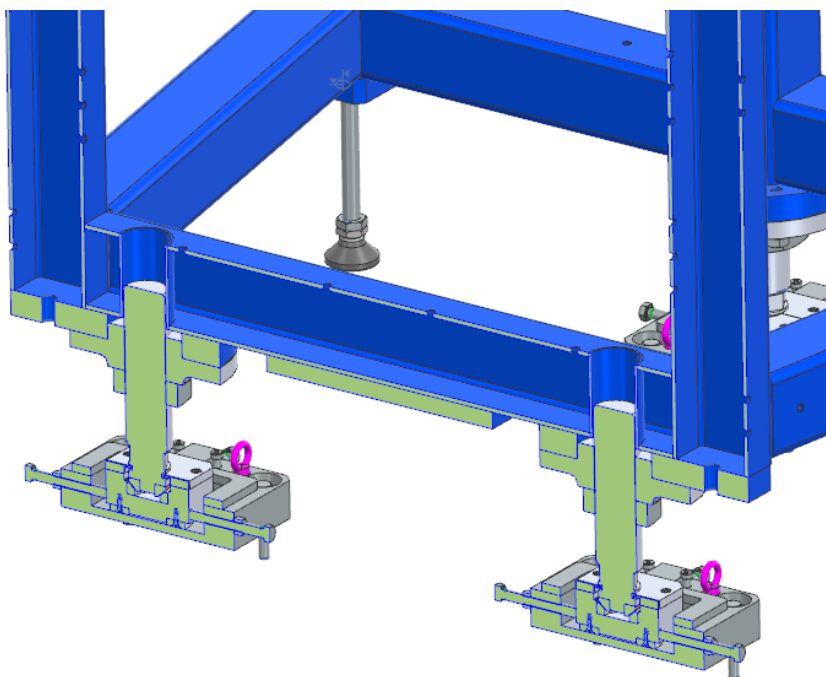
vue de coupe de deux pieds réglables supportant un châssis
